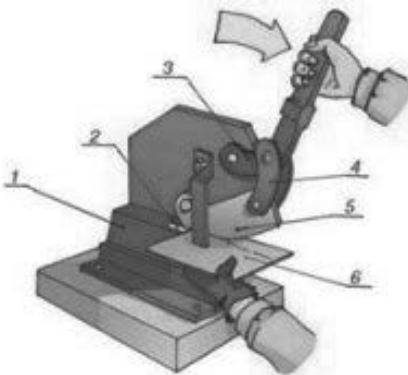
Настільні ручні важільні ножиці: 1 – основа ножиць; 2 – нижній нерухомий ніж; 3 – важіль; 4 – з'єднувальна планка; 5 – верхній рухомий ніж; 6 – заготовка
